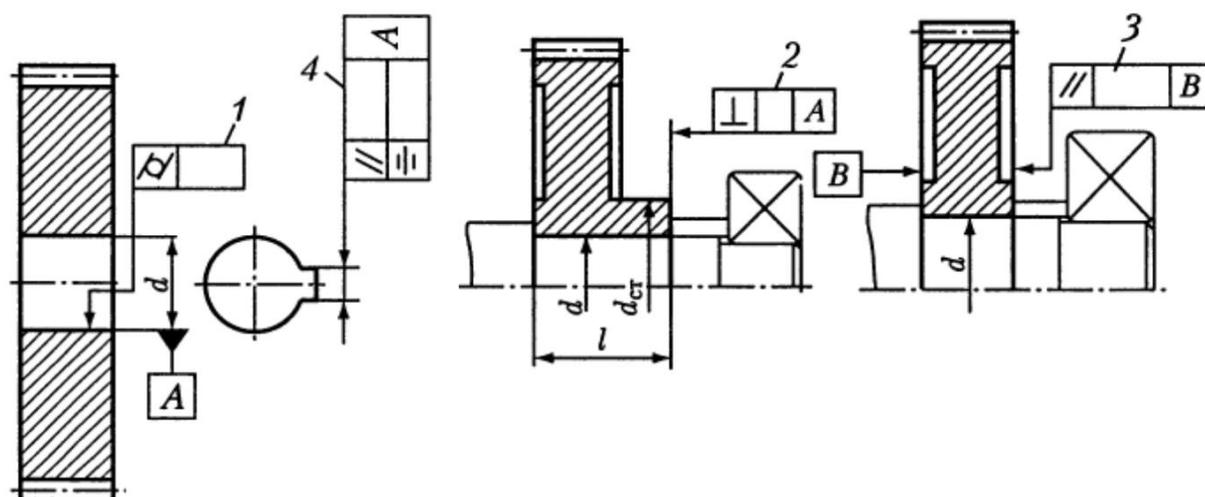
Допуски формы и расположения поверхностей колес
